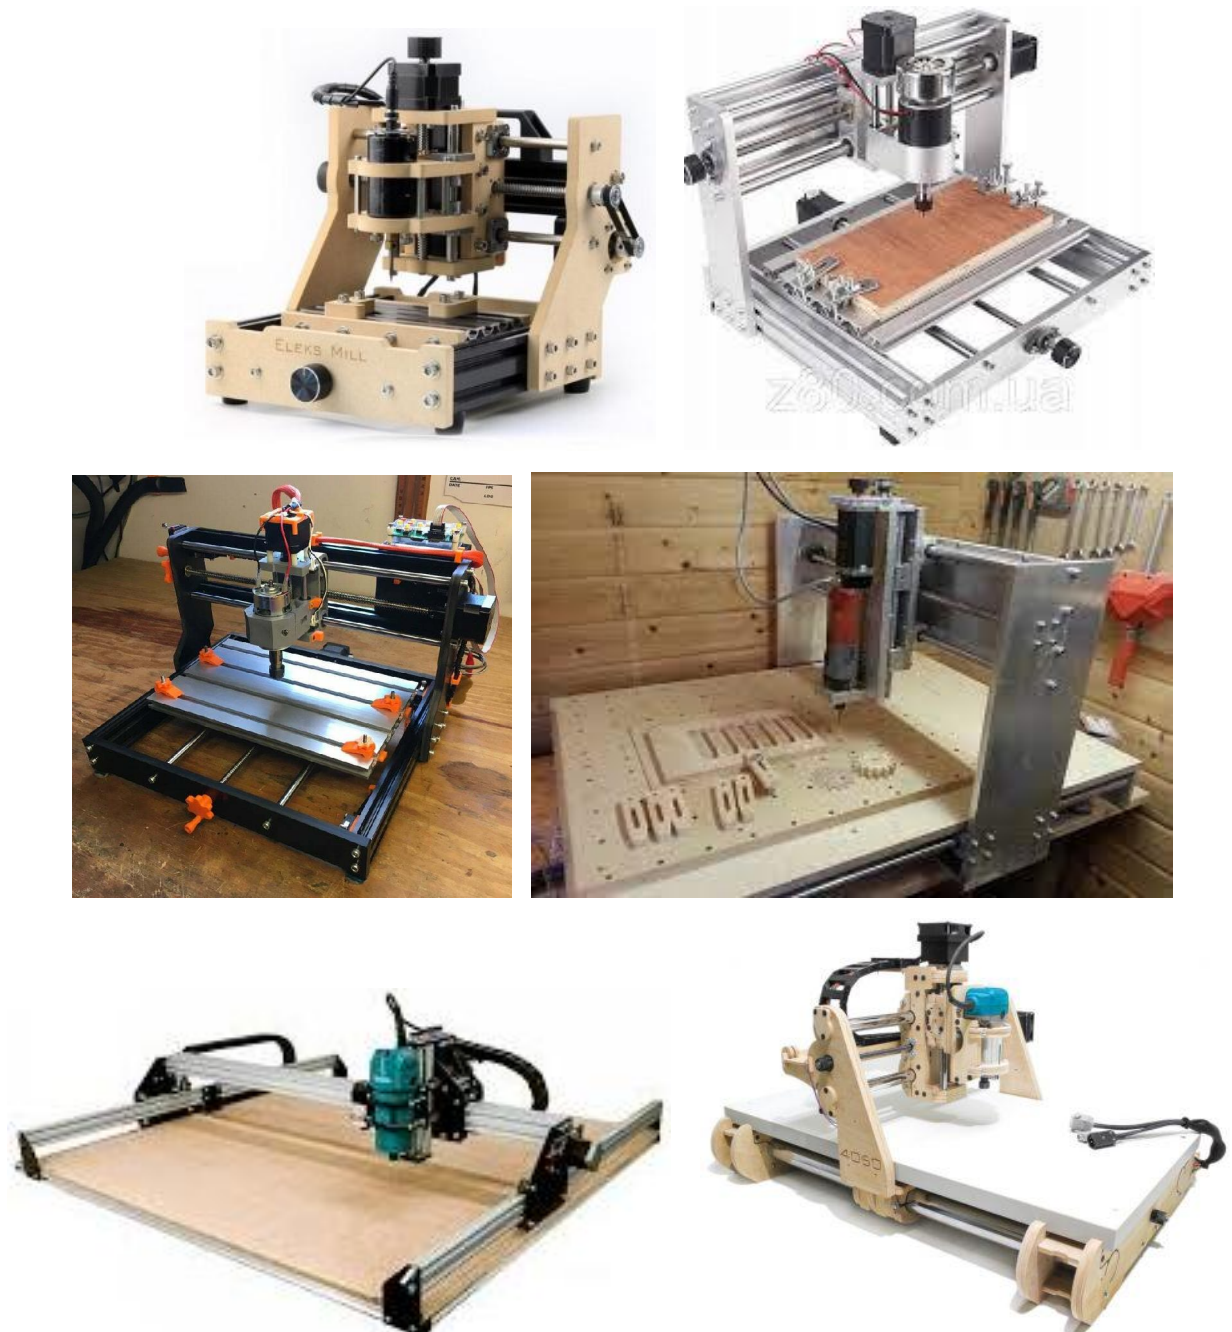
Зовнішній вигляд конструкцій ЧПУ-фрезерів.
